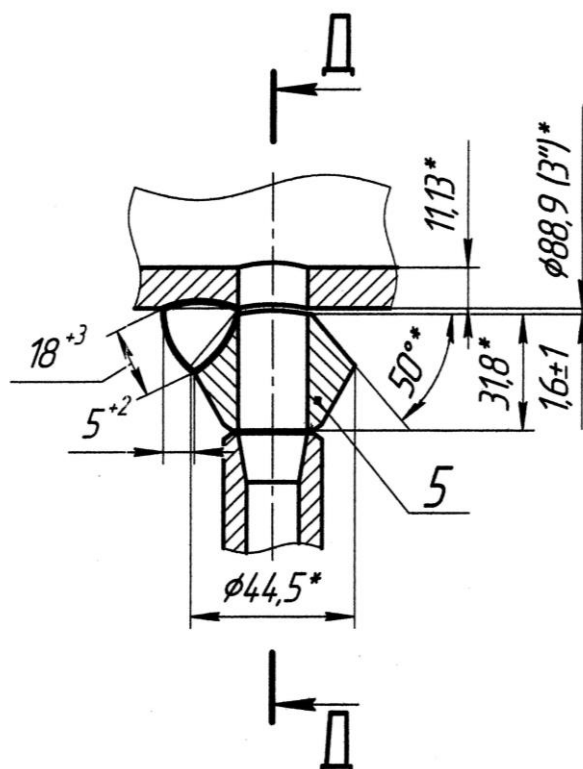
Общий вид соединения трубы 1 и бобышки 5
